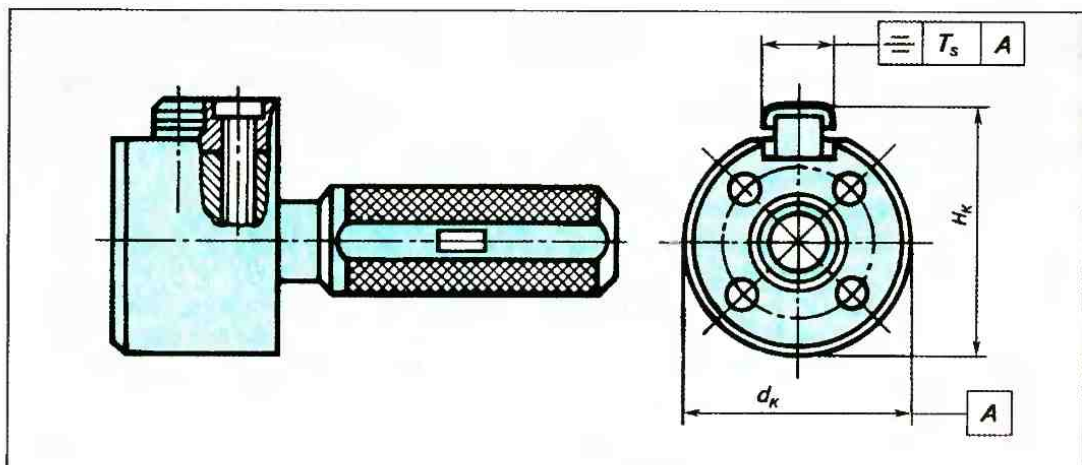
Комплексный проходной шпоночный калибр-пробка
